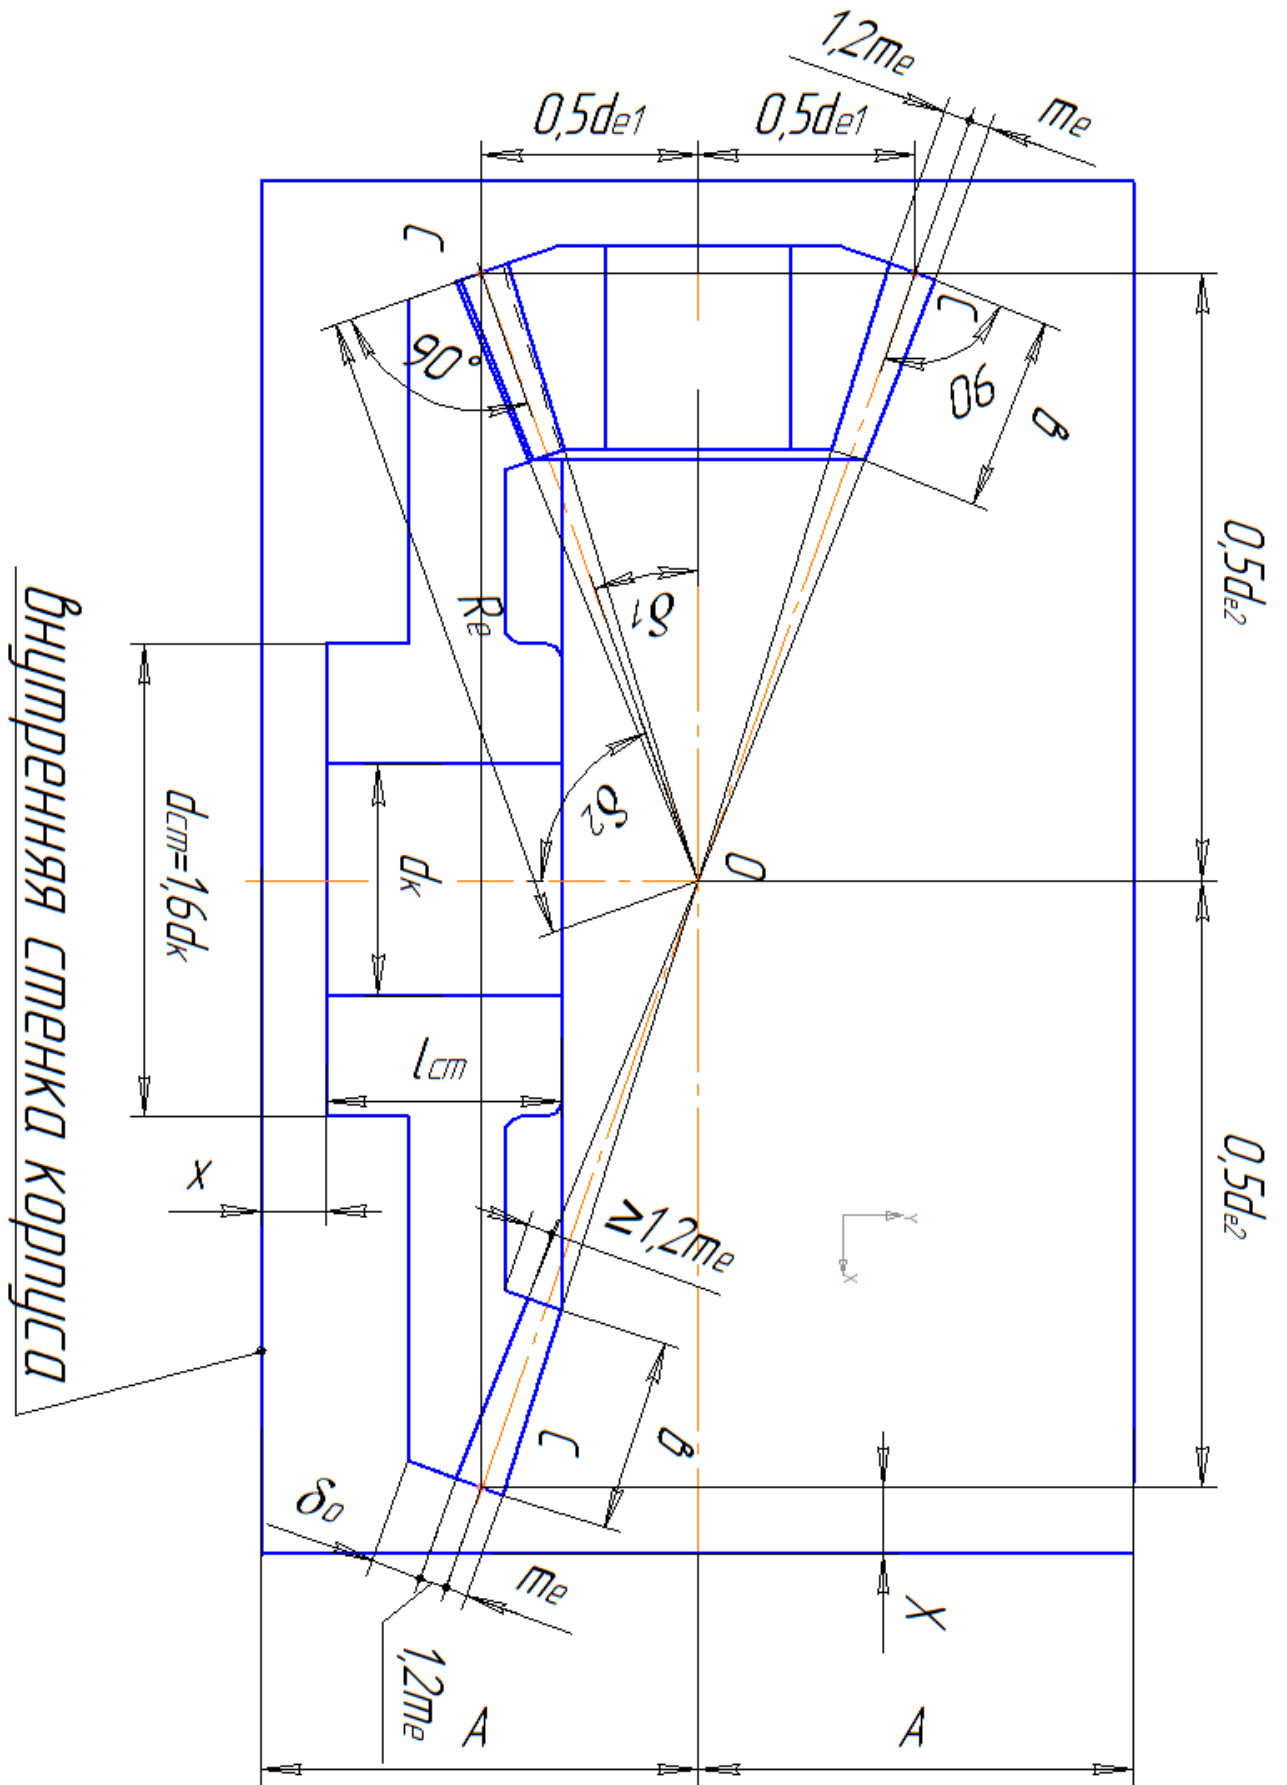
Первый этап эскизной компоновки конического редуктора
